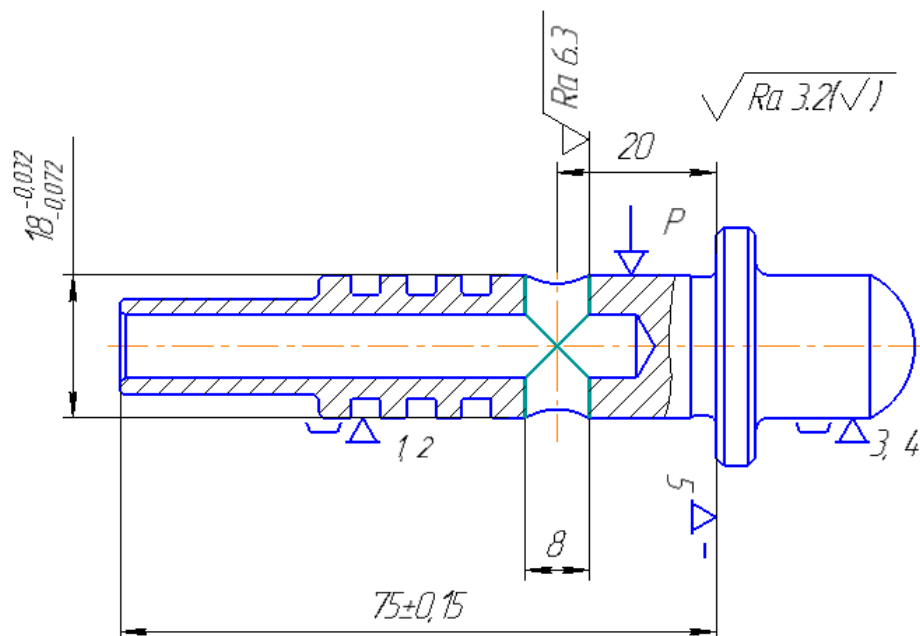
Схема базування заготовки на операції свердлильній з ЧПК
